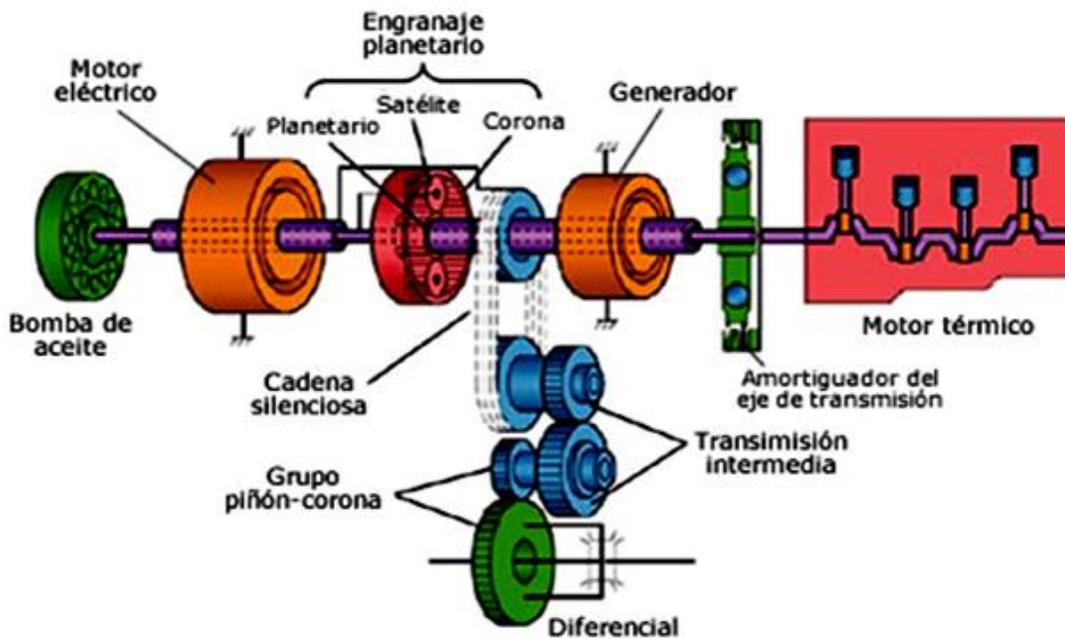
Conjunto de engranaje planetario usado en la transmisión TOYOTA.
